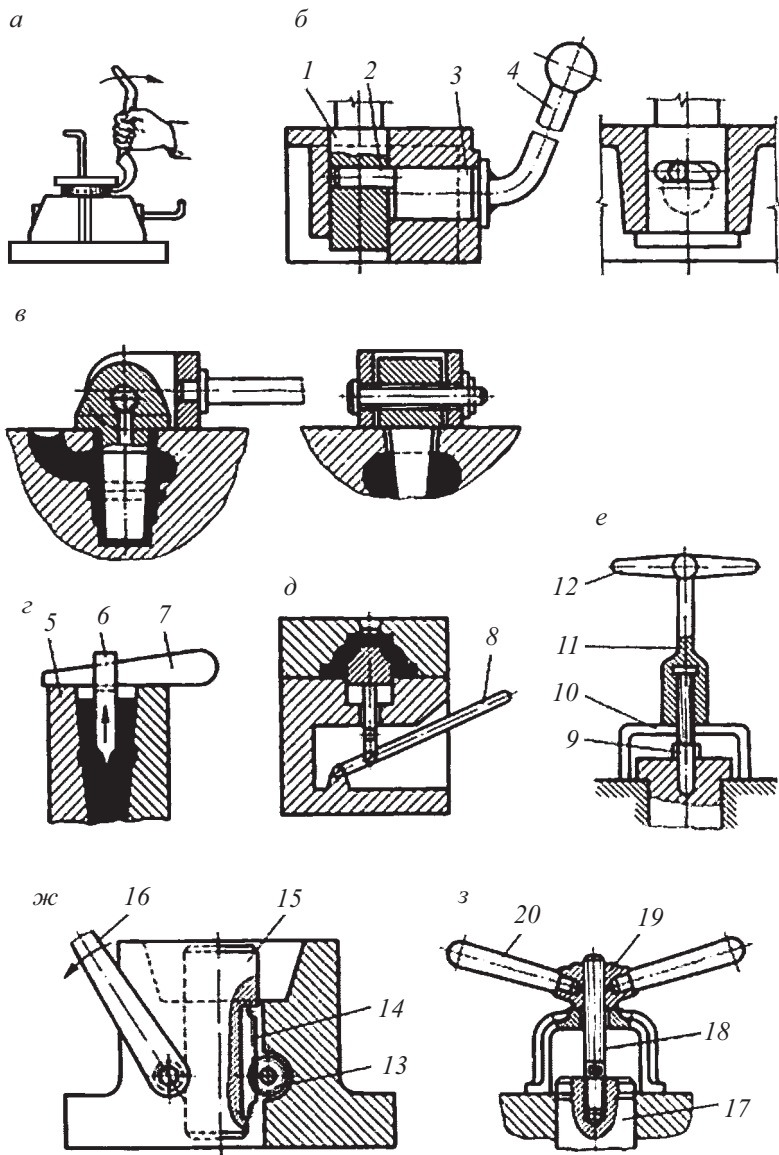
Ручные приспособления и механизмы (а – з) для извлечения металлических стержней
